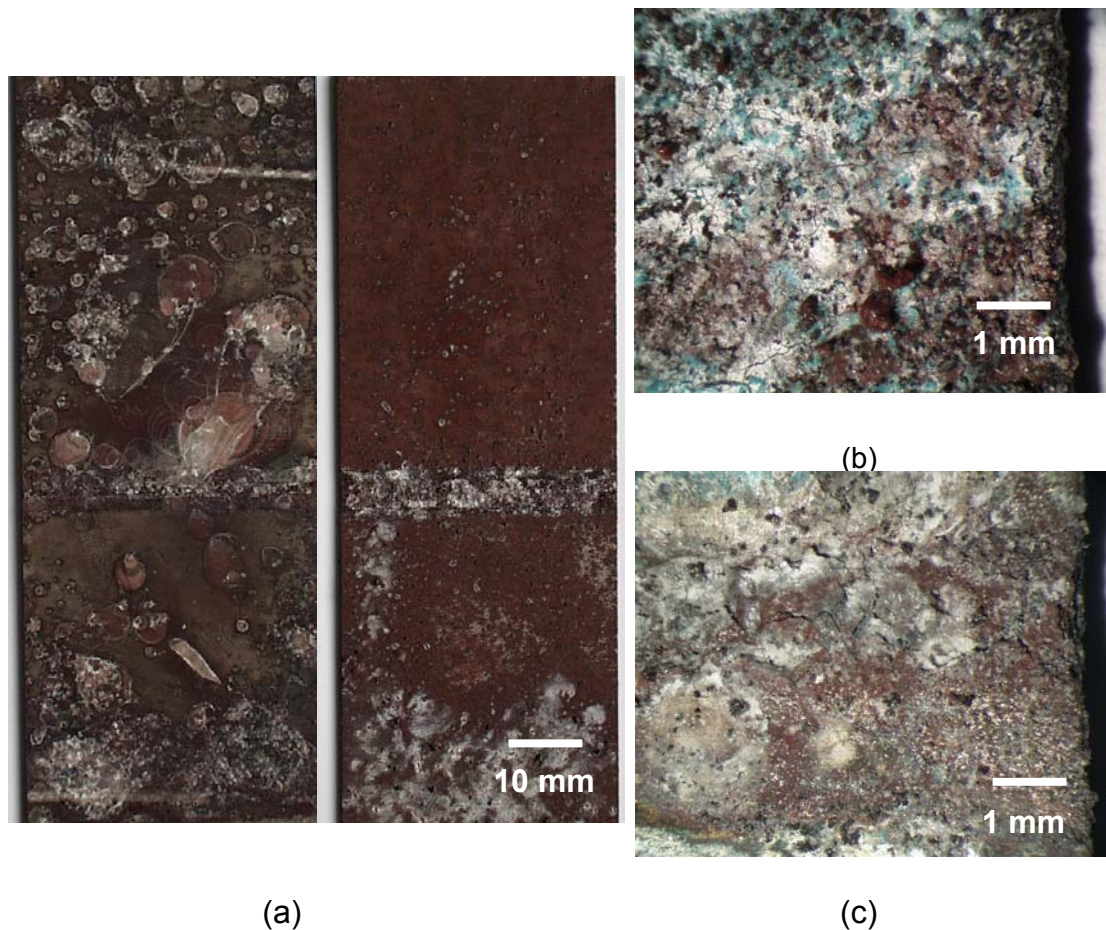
Junta soldada por FSW da liga 2024-T351 após ensaio de corrosão por esfoliação por um período de 48 horas. (a) Face e raiz da solda. (b) Ataque intenso na face. (c) Raiz da solda com trincas na região da lente de soldagem.
